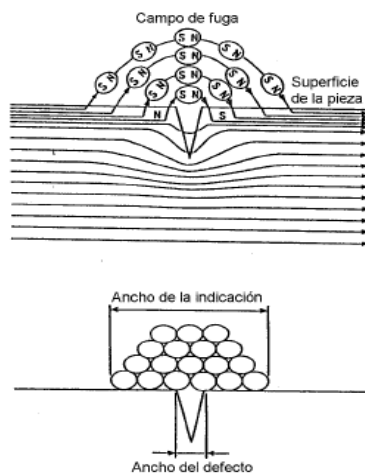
Campos de fuga en la superficie de la pieza inspeccionada.
